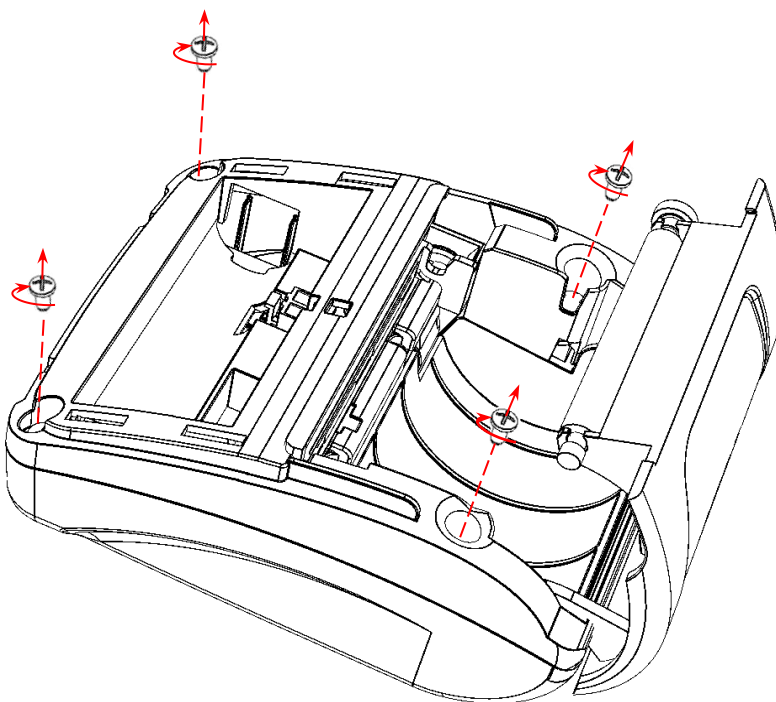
Винты крепления верхней и нижней части корпуса ККТ
